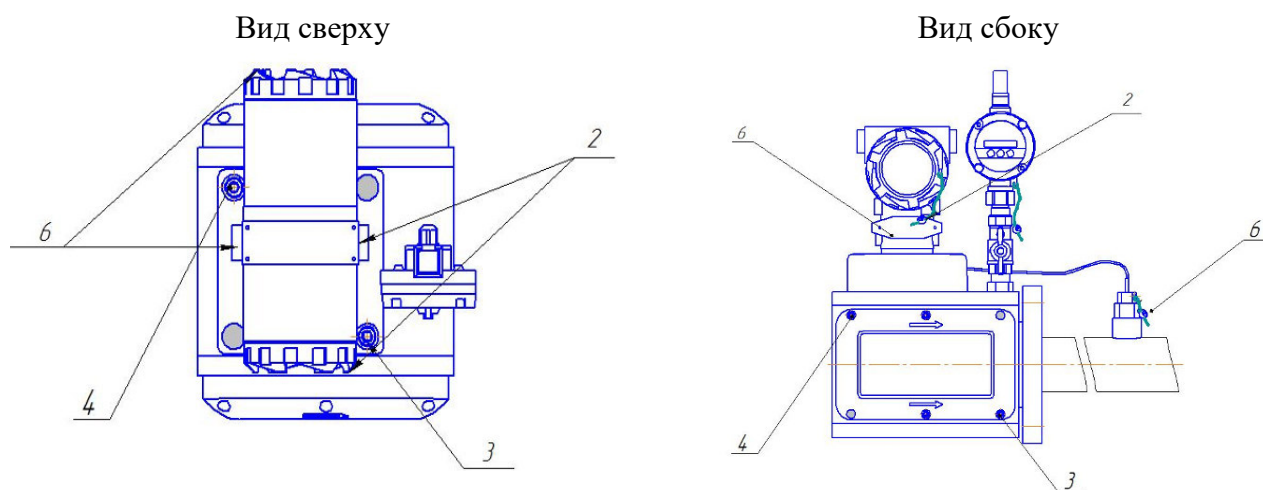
Корпус прямоугольного сечения с совмещенными защитными крышками
